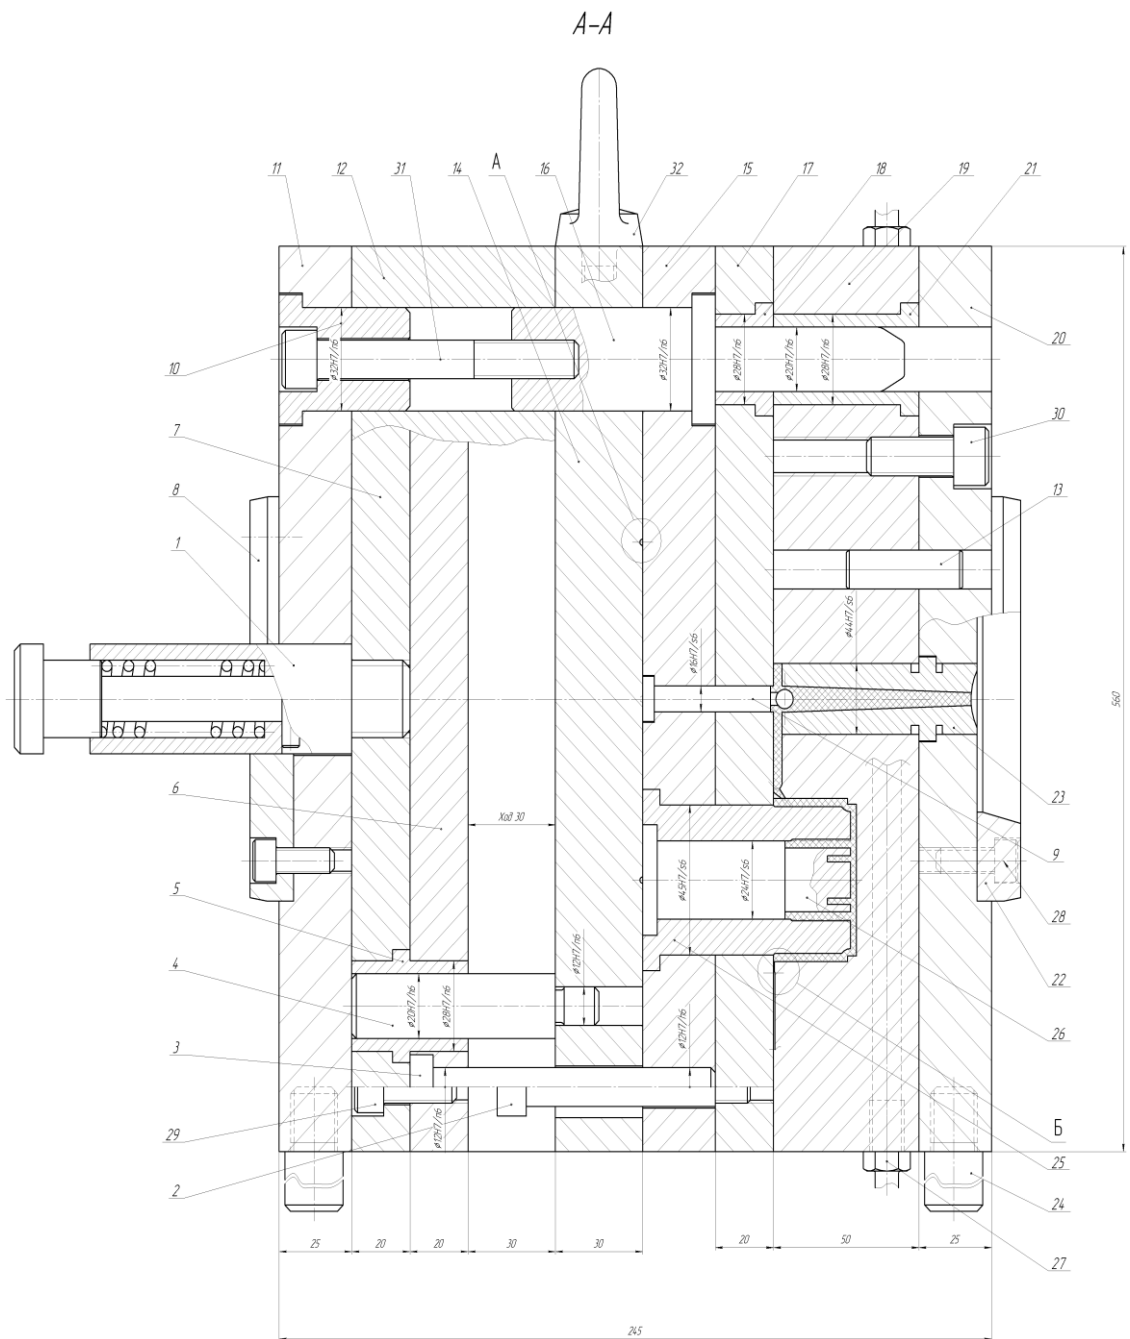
Литьевая форма новой технологии изготовления детали «Крышка бака топлива» (в разрезе А-А)
